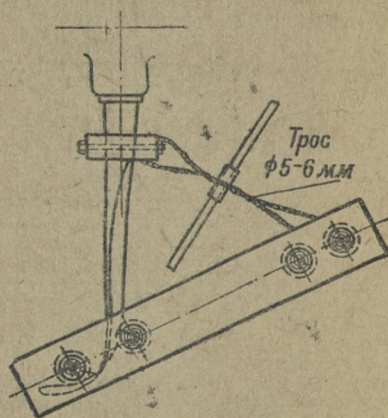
Приспособление для правки погнутой лопасти при помощи троса
